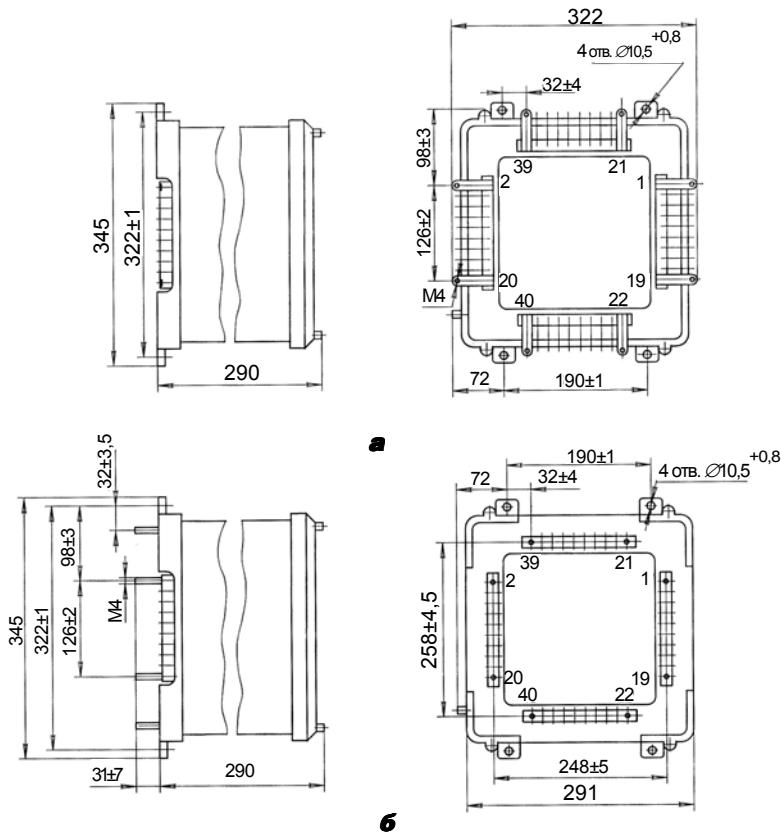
Габаритные, установочные и присоединительные размеры комплектов защиты типа КЗ-13.
